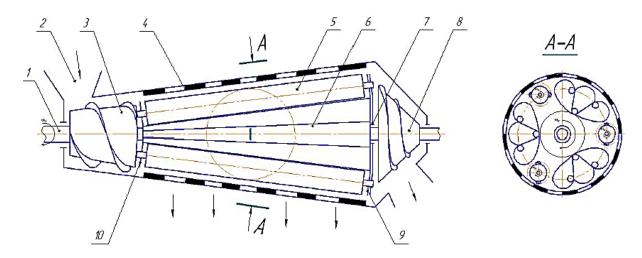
Схема молотильно-сепарирующего устройства: 1 — опорно-приводной вал аксиального ротора; 2 — загрузочная воронка; 3 — шнек-питатель; 4 — коническое решетчатое подбарабанье; 5 — планетарный валец с бичами; 6 — упругодемпфирующий рабочий орган; 7 — планетарный привод; 8 — ворохоотводящий шнек; 9 и 10 — диски-водила с подшипниками /
